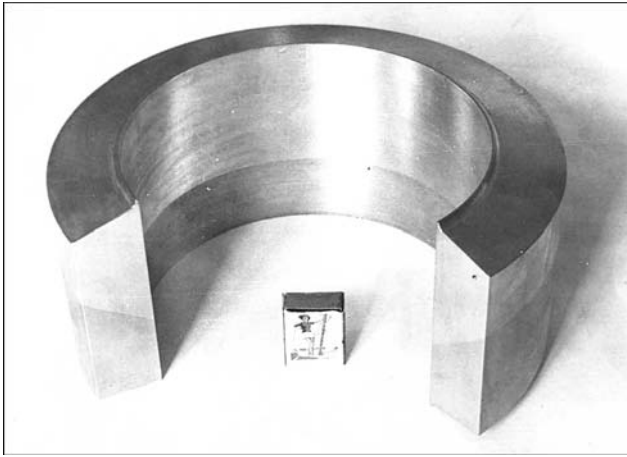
Переходный элемент (диаметр 350×50 мм) для сварки трубы из стали 12ХМФ с трубой из стали 10Х18Н10Т, изготовленный АВП под давлением
